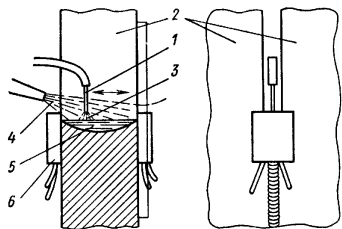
Схема сварки вертикальных и наклонных швов с принудительным формированием:
